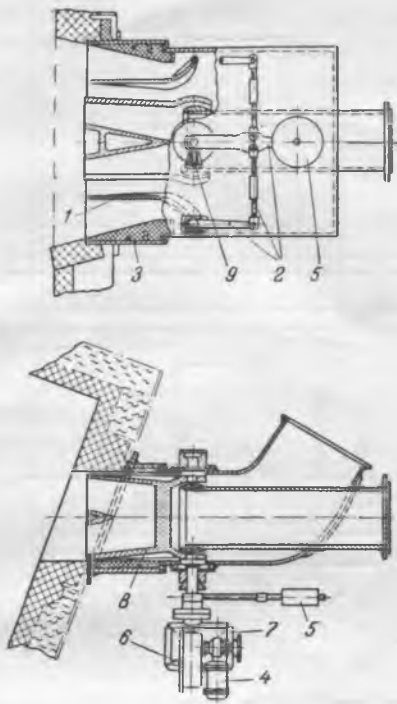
Поворотная горелка новой конструкции (УП-5).
